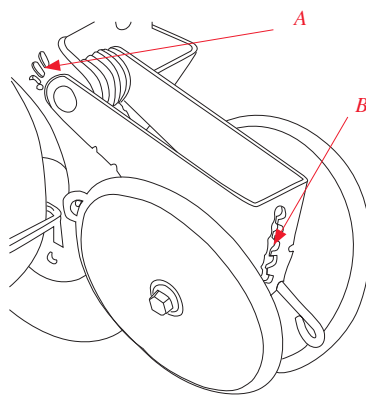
Колеса загортання насіннєвої борозни сівалки
